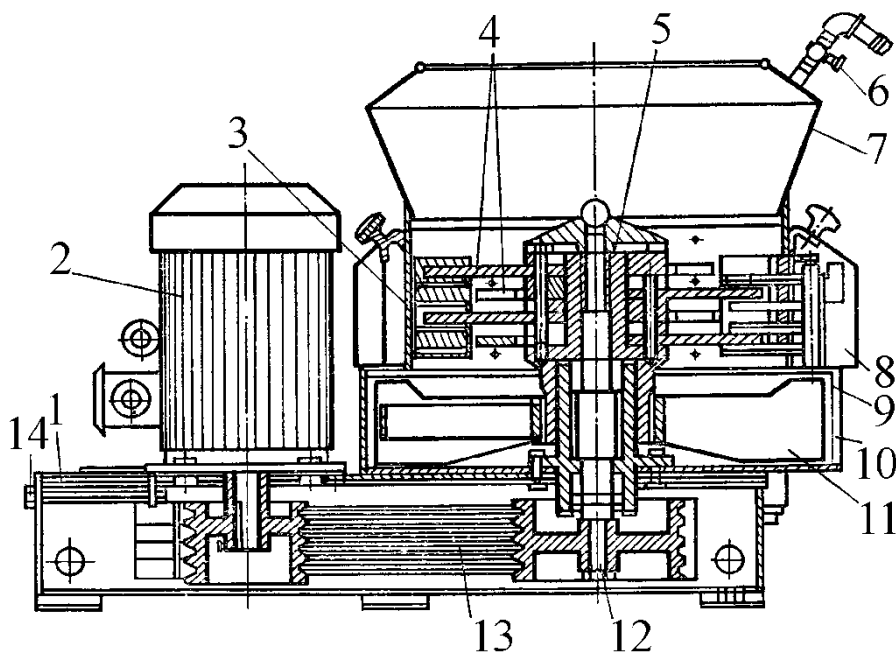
Общий вид измельчителя-смесителя кормов ИСК-3А:
